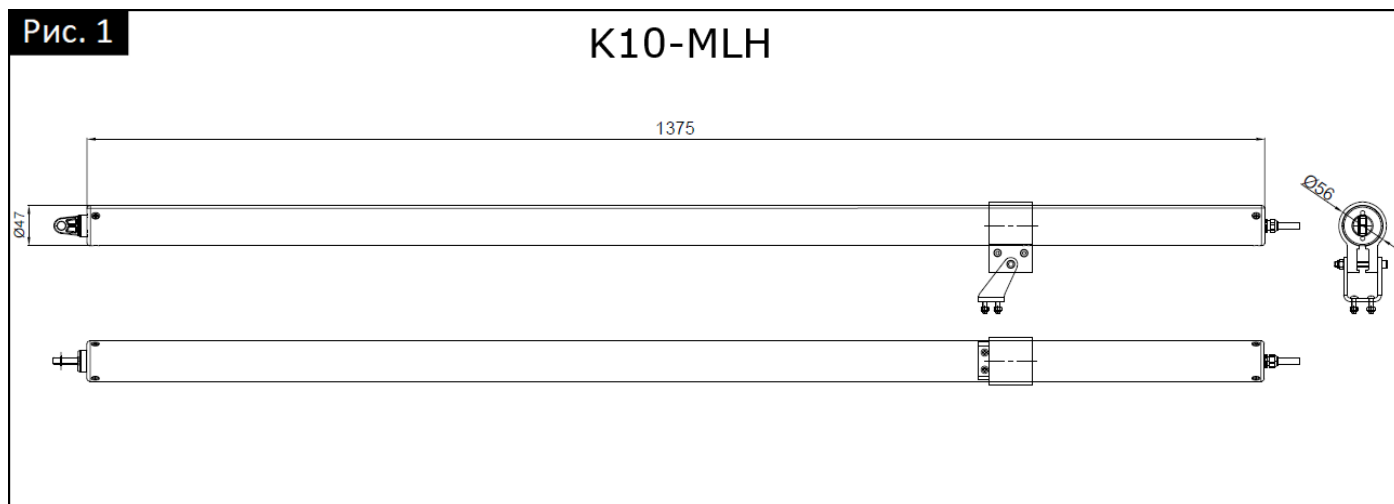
Габаритные размеры привода K10-MLH 24В 1000 мм.
